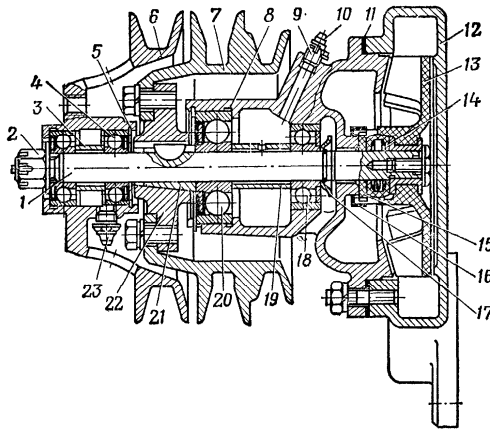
Водяний насос: 1 – вал насоса; 2 – гайка; 3 і 19 – розпірні втулки; 4 – підшипник вентилятора; 5 – упорна шайба; 6 і 7 – шків; 8 – корпус підшипників; 9 – пробка; 10 і 23 – маслянки; 11 – прокладка; 12 – корпус насоса; 13 – крильчатка; 14 – ущільнювач; 15 – ущільнювальна шайба; 16 – обойма; 17 – відбивач; 18 і 20 – підшипники вала насоса; 21 – конусна втулка; 22 – маточина шків водяного насоса
